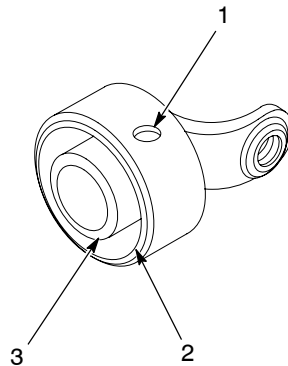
Installazione di gruppi di montaggio su tubo
